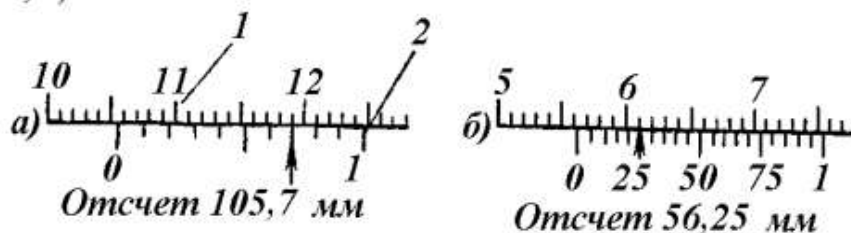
Примеры отсчета размеров по нониусу штангенинструмента: 1 – основная шкала; 2 – шкала нониуса
